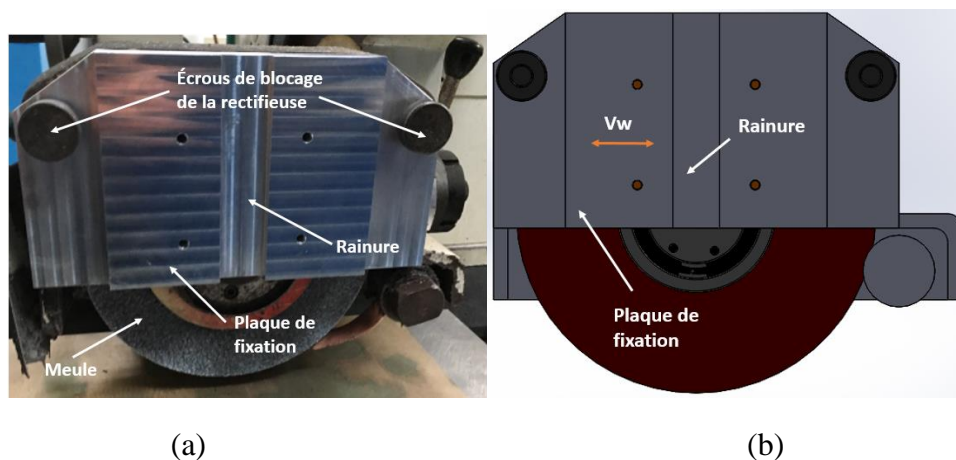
(a) Plaque en aluminium de fixation de l'outil de galetage sur la rectifieuse, (b) CAO de la plaque de fixation.
